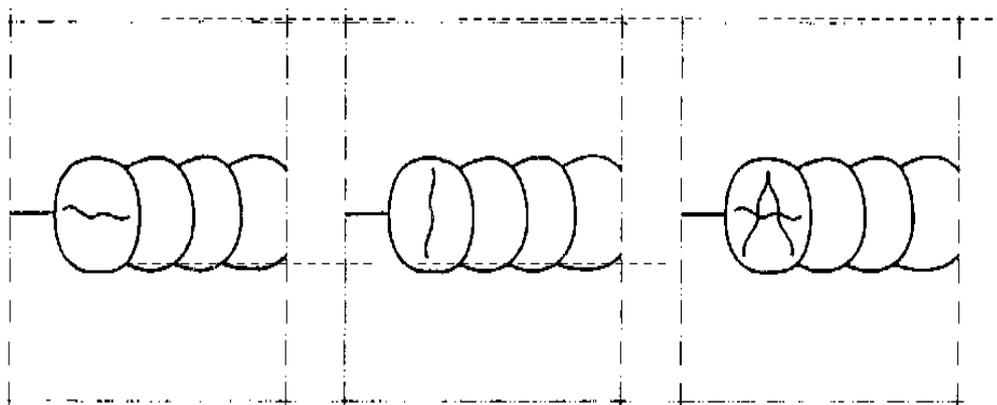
Кратерная трещина сварного соединения
